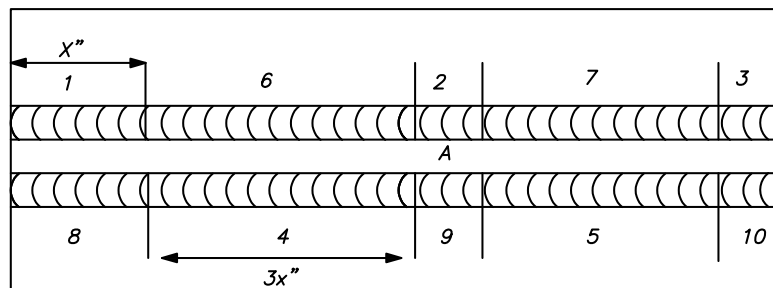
Secuencia de soldadura en una junta en T (Masubushi, 1982)
